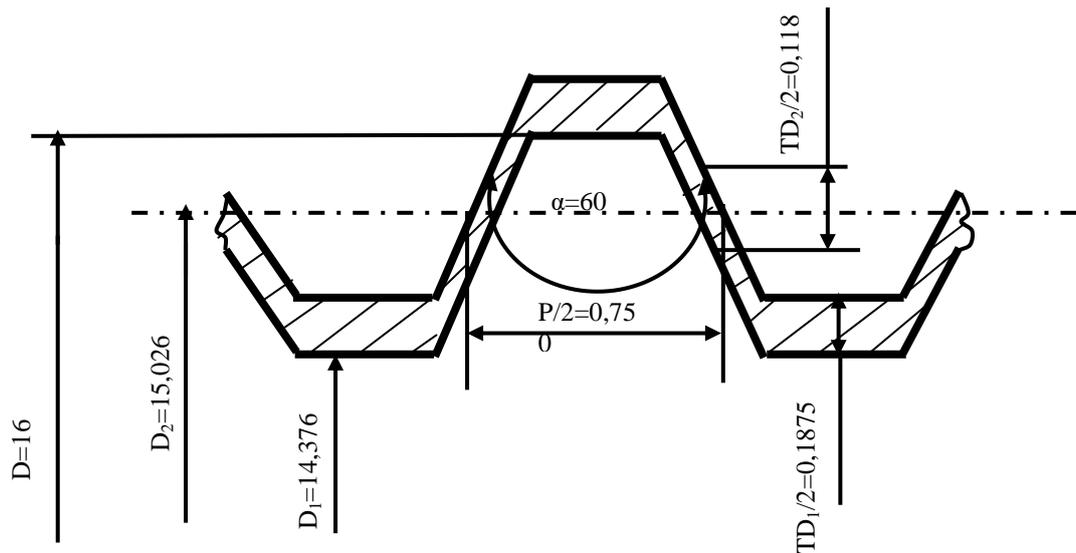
Схема розташування полів допусків метричної нарізі M16x1,5-7H.
